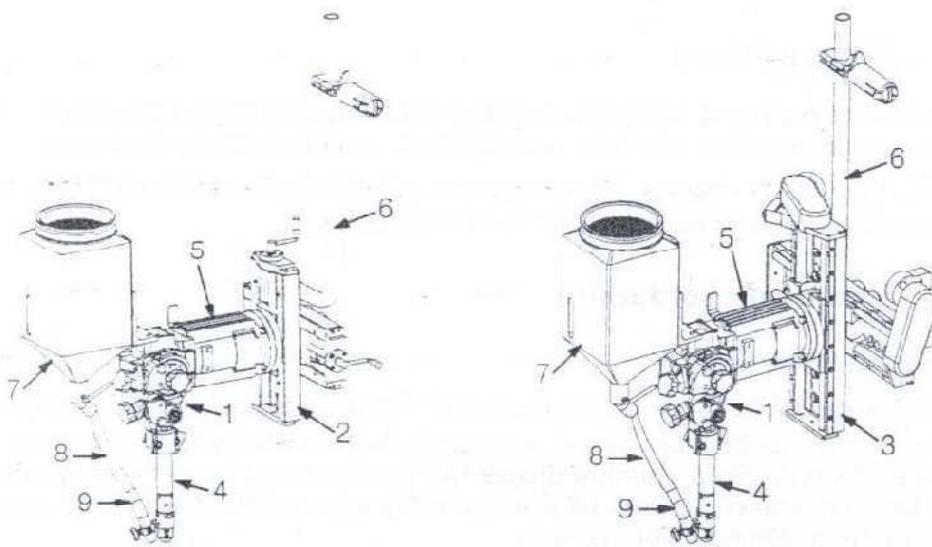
15 Componentes Principales del Cabezal de Soldadura Manual/Motorizado
